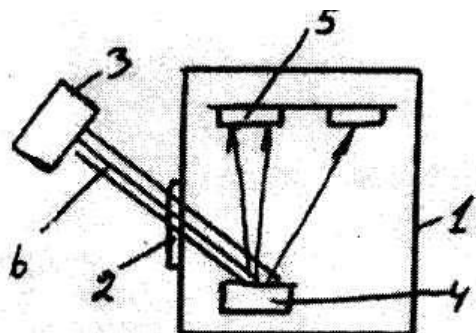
Принципова схема установки лазерного напилення покриттів:
